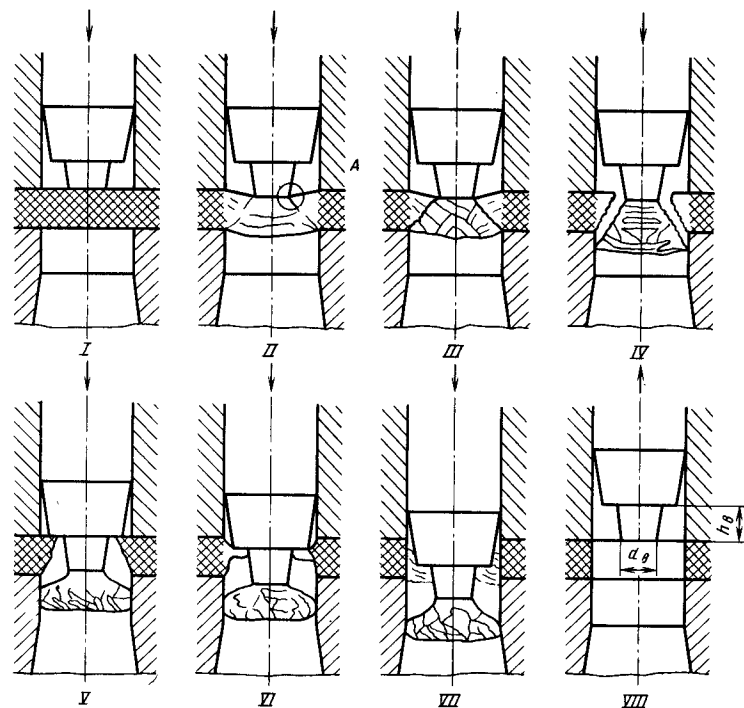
Схемы пробивки отверстий пуансонами с предразрушающими выступами
